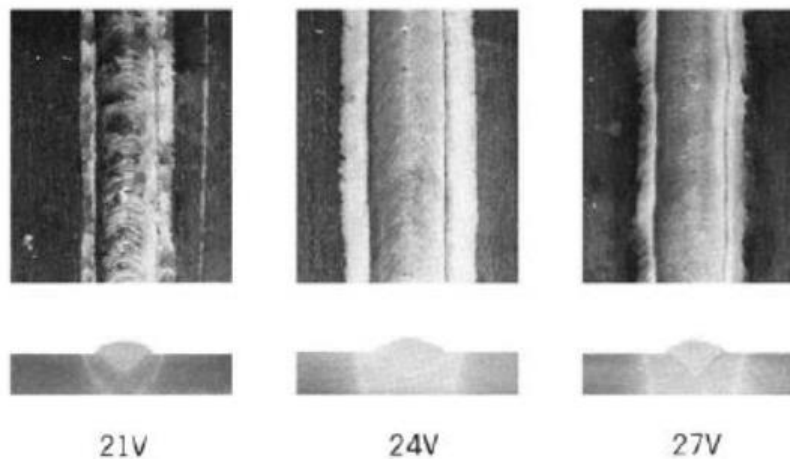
Efeito da tensão de soldadura na penetração da solda [29].
